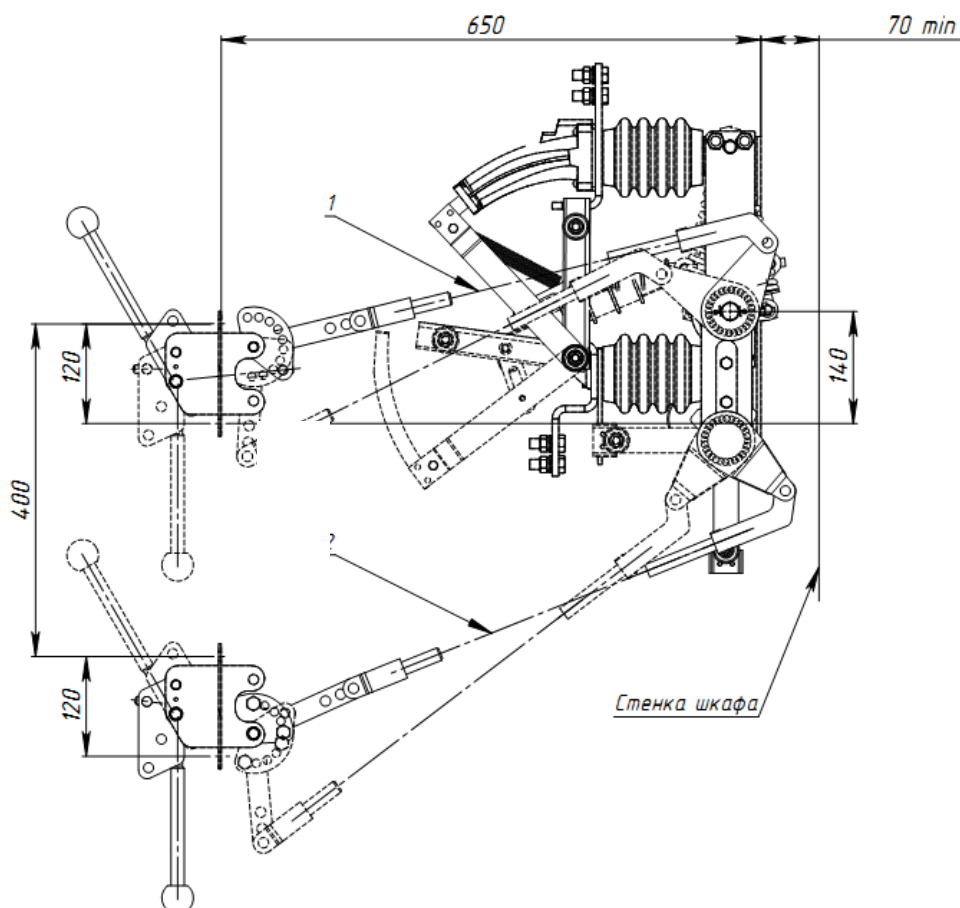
Схема установки механизма блокировки для выключателей с плавкими предохранителями
